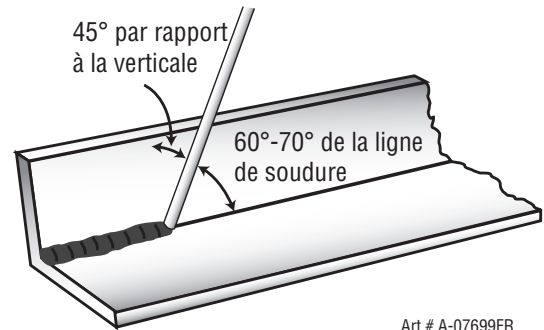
Position de l'électrode pour une soudure d'angle HV
